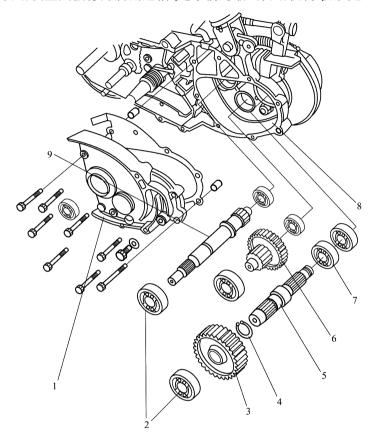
78 后减速箱 1—齿轮器盖;2—轴承;3—齿轮;4—卡簧;5—输出轴;
